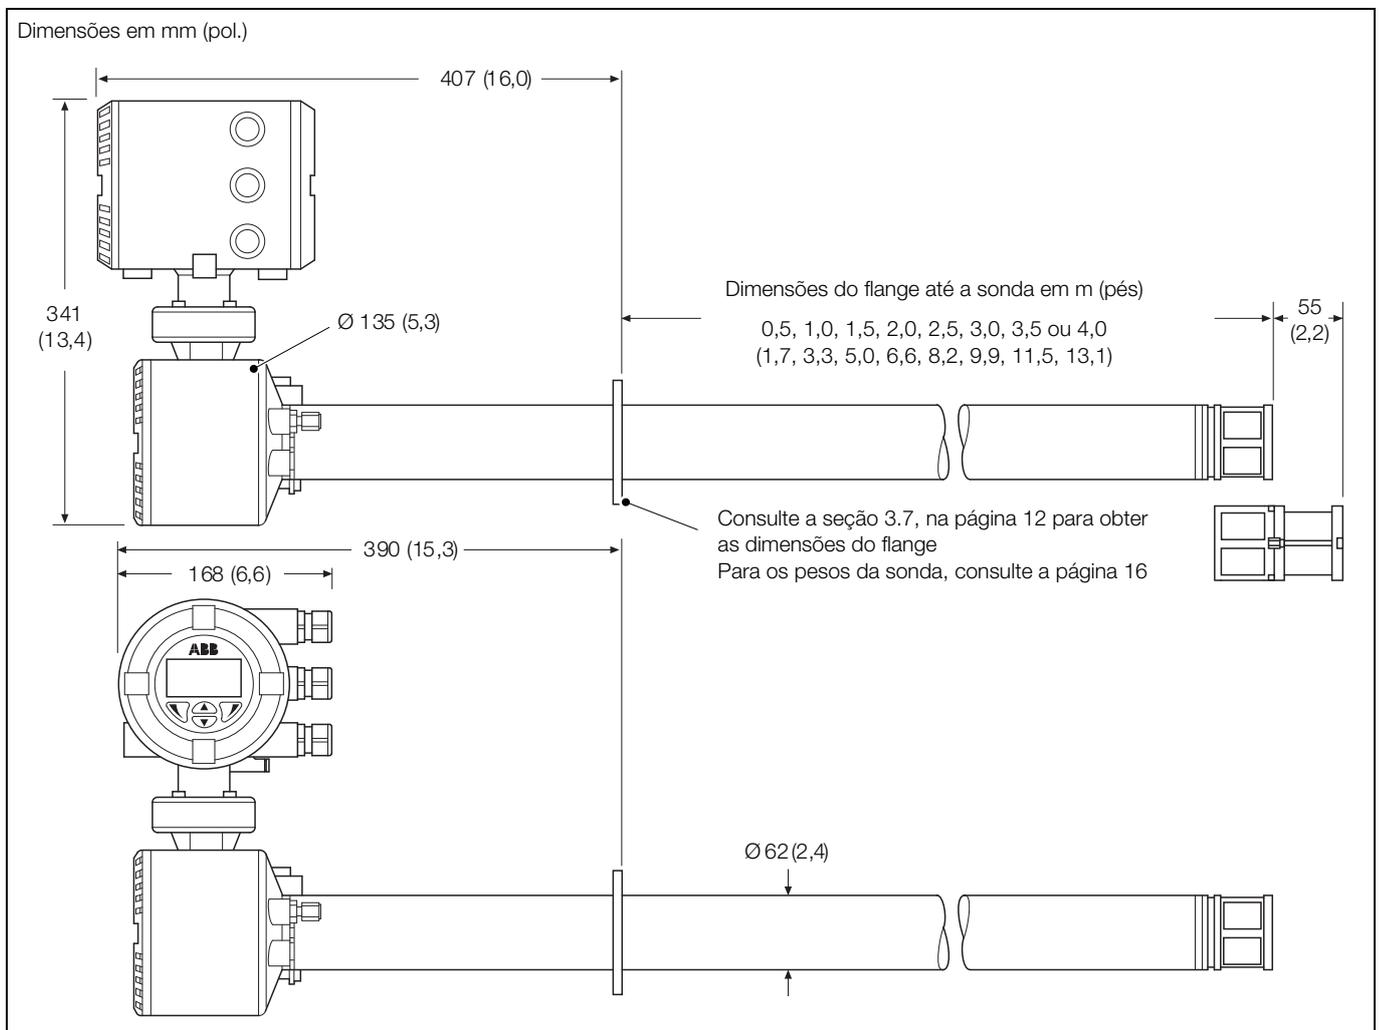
Dimensões gerais – sonda integral Endura AZ20
